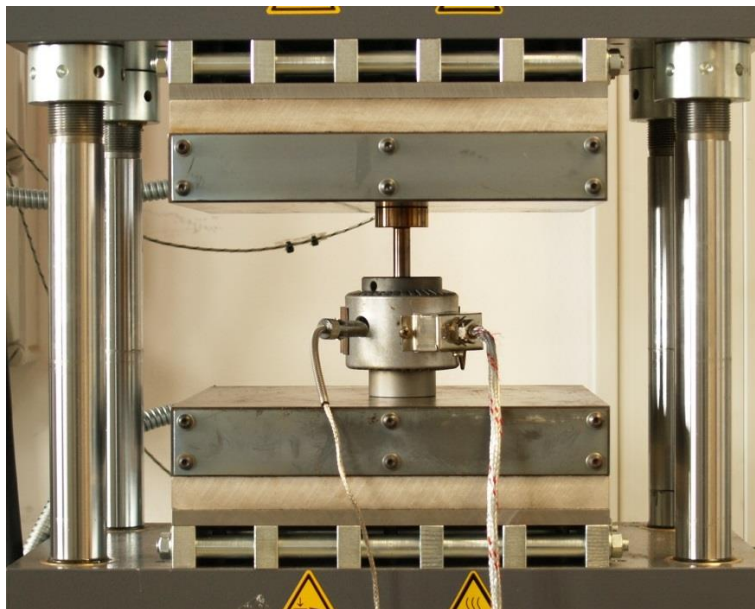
Beheizbares Werkzeug in der Hydraulikpresse
